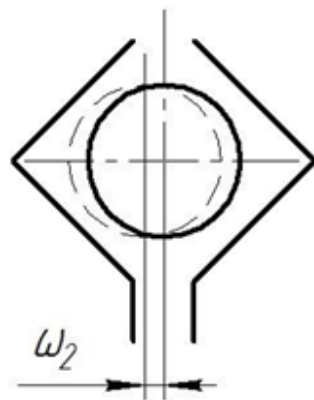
Похибка положення заготовки в захватному пристрої
